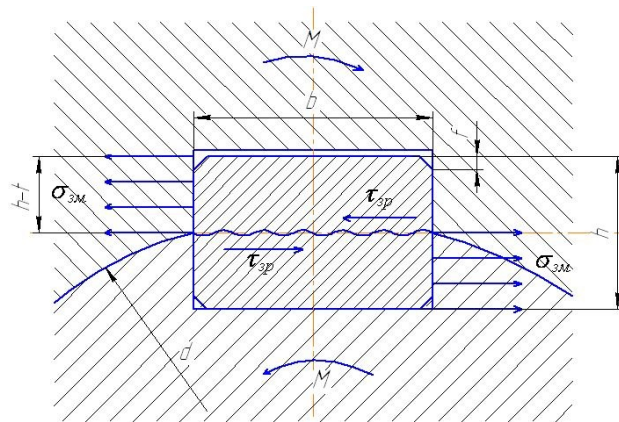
Розрахункова схема з'єднання призматичною шпонкою
